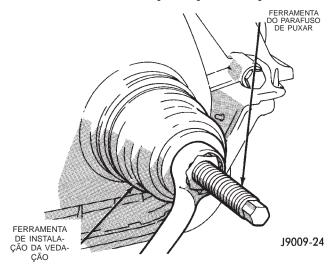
Instalação de Vedação de Óleo da Tampa da Caixa de Regulagem
